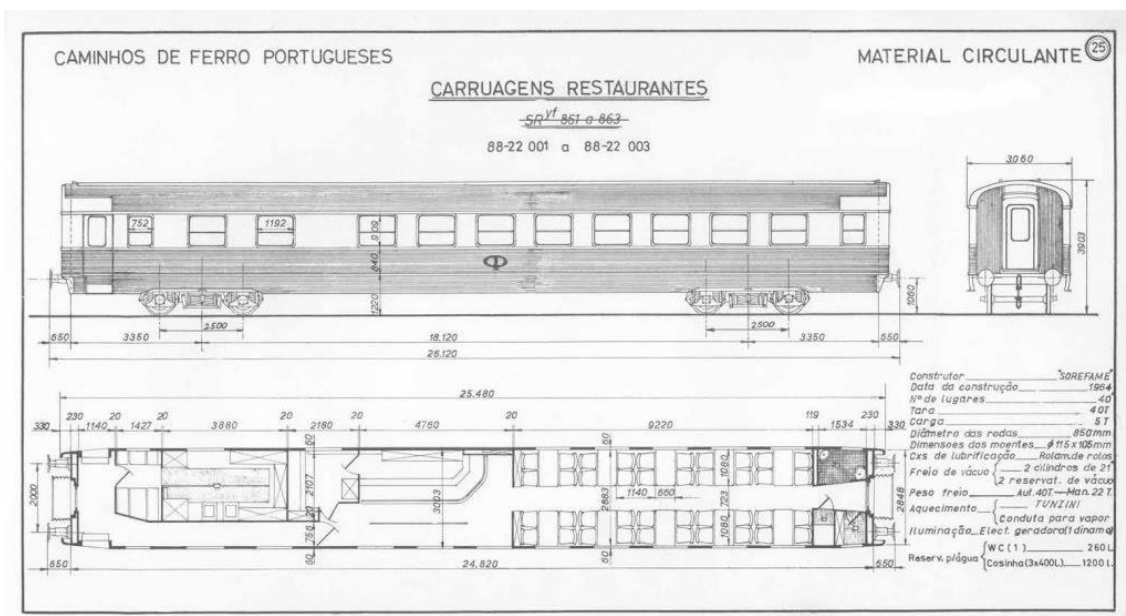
Plano coche Restaurante – Bar de Sorefame
